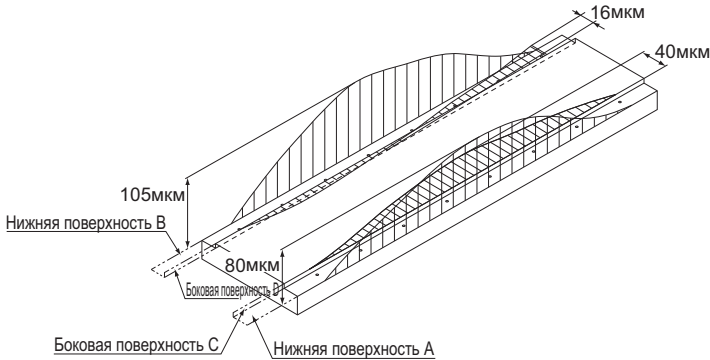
Точность монтажной поверхности, на которую устанавливается направляющая LM (обработка: только фрезерование)
